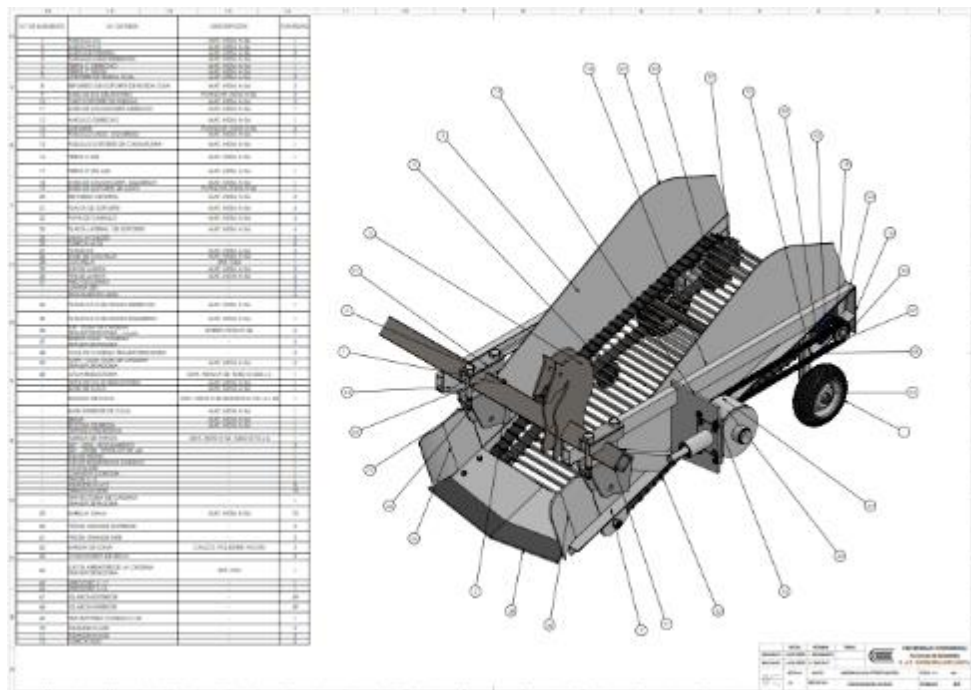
Detalle ensamblado de máquina cosechadora.
